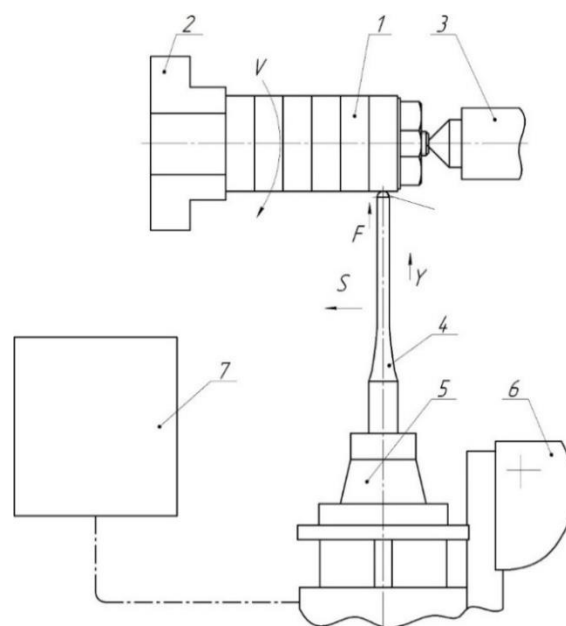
Схема ультразвуковой упрочняющей обработки: 1 – заготовка; 2 – патрон; 3 – задний центр; 4 – ультразвуковой инструмент с полуцилиндрическим наконечником; 5 – магнитострикционный преобразователь в корпусе ДТМ; 6 – резцедержатель токарного станка; 7 – ультразвуковой генератор
